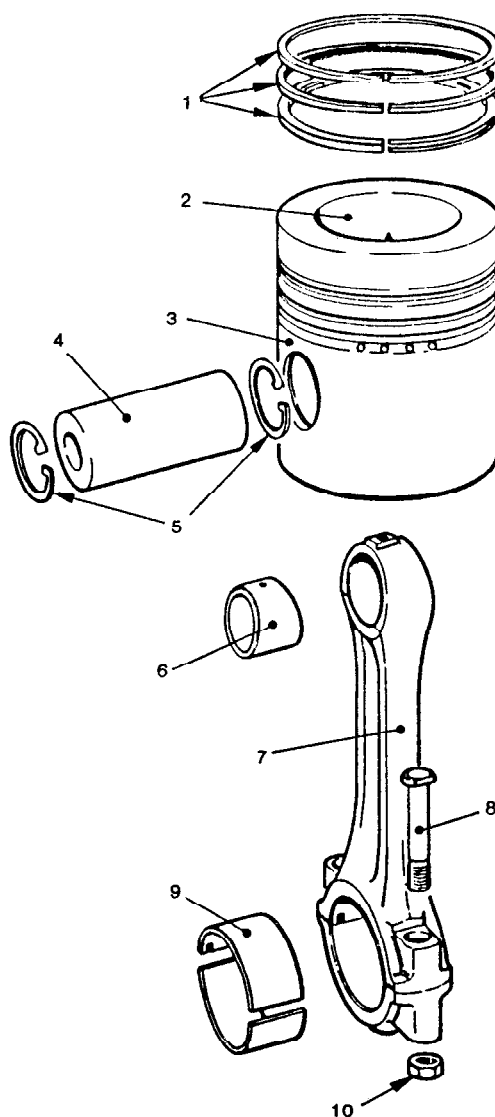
Conjunto de pistón y biela: 1 anillos de pistón, 2 cámara de combustión, 3 pistón, 4 pasador de pistón, 5 arillos seguros, 6 buje para el pasador de pistón, 7 biela, 8 tornillo, 9 metal de cojinete, 10 tuerca
